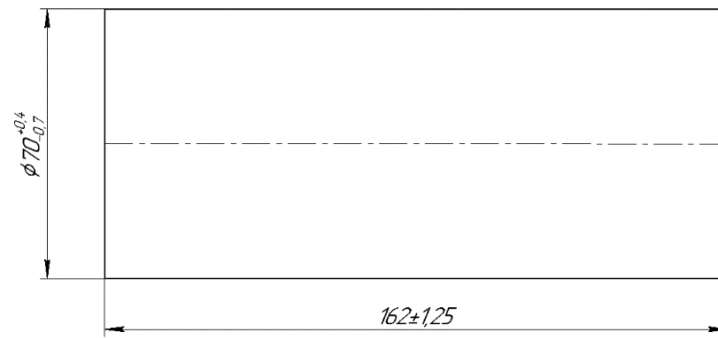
Ескіз заготовки деталі «Вал-шестерня»
